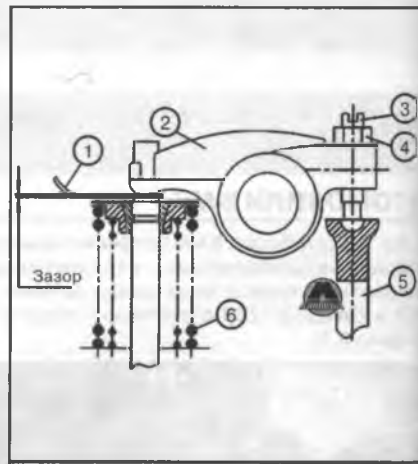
Регулировка зазора между коромыслом и клапаном: 1. Щуп; 2. Коромысло; 3. Регулировочный винт; 4. Контргайка; 5. Штанга толкателя; 6. Пружина клапана.
